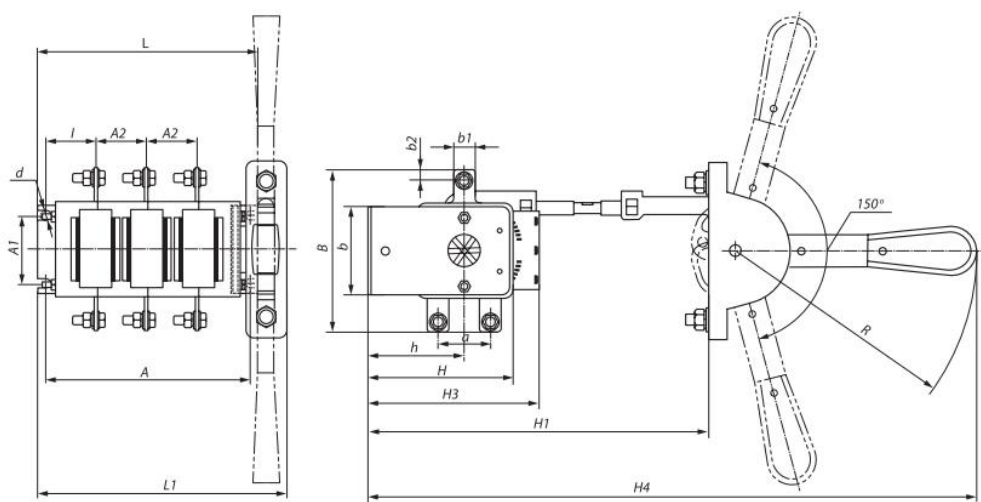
Выключатель-разъединитель универсальный трехполюсный на два направления с д/г камерами, передняя смещенная несъемная левая/правая рукоятка
